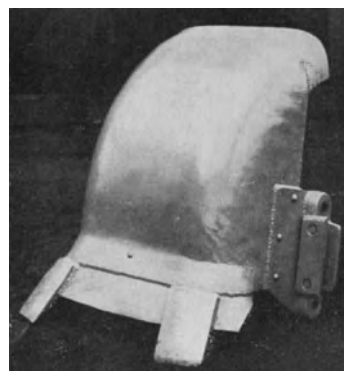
Vollständig geschweißter Eimer (I.M.G.).
